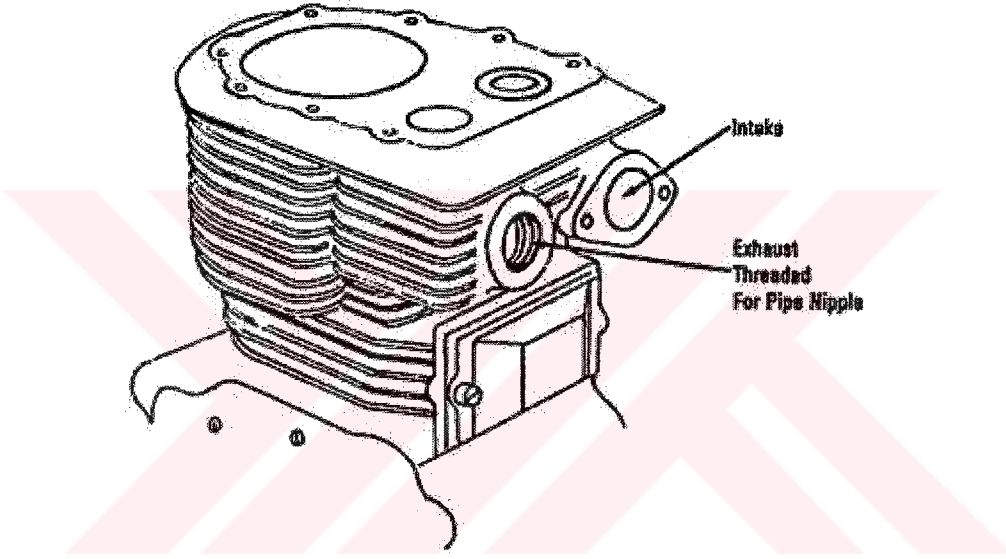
Hava giriş çıkışı (Miller & Miller, 1993)
